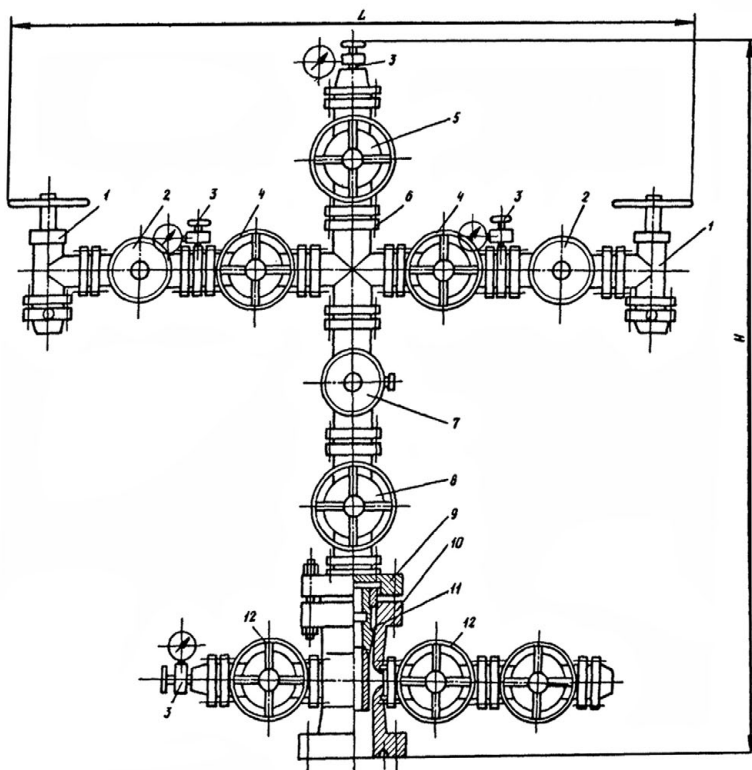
Фонтанная арматура крестовая АФ6В-80/65х35К2:
